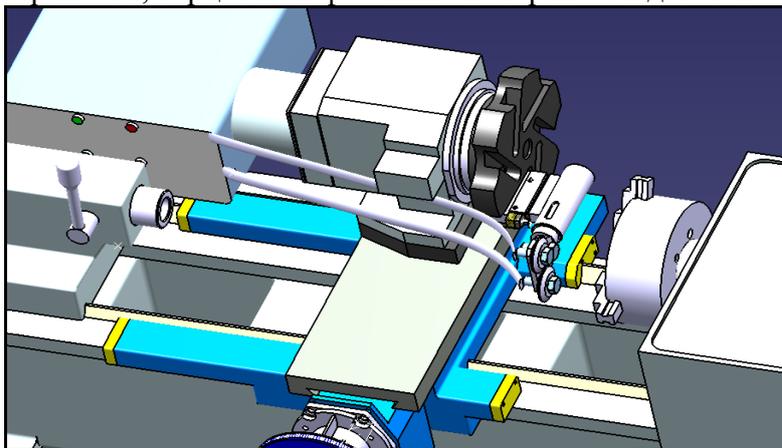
Фрагмент расположения оборудования, инструмента и оснастки электромеханической обработки на токарно-винторезном станке с ЧПУ модели 16K20Ф3М
